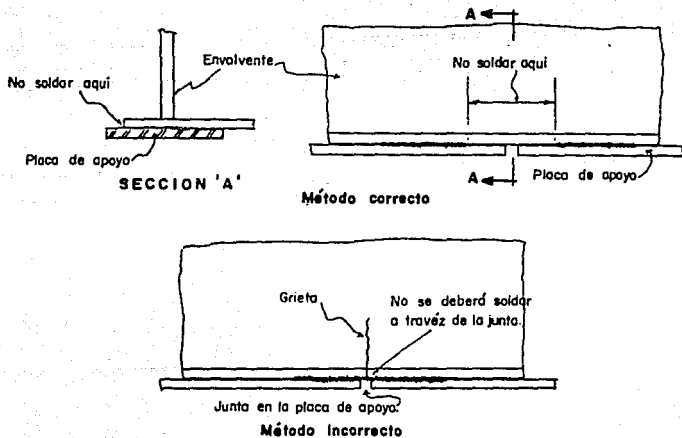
LUGARES DONDE SE DEBE OMITIR SOLDADURA
